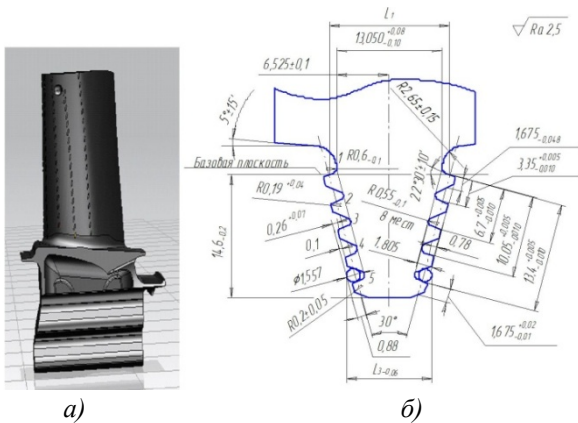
Общий вид рабочей лопатки турбины ГТД (а) и елочный профиль замка (б)
